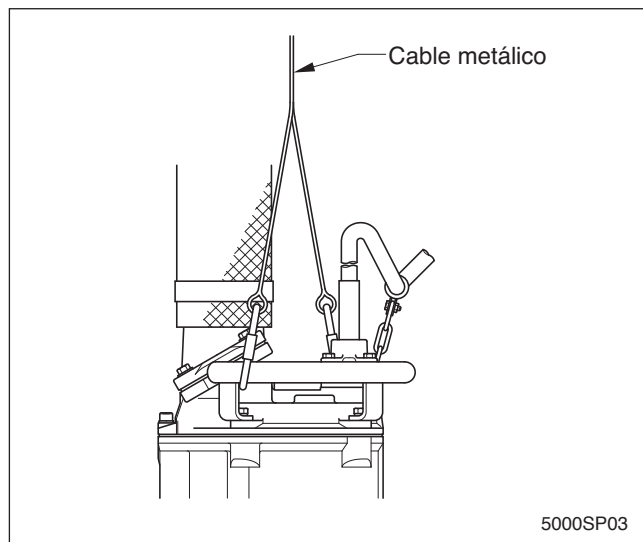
LEVANTAMIENTO DE LA BOMBA
